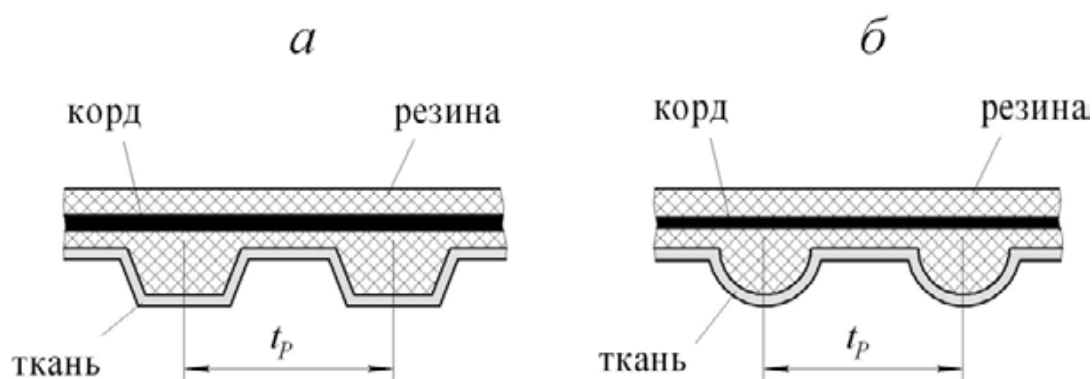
Сборочный зубчатый ремень: *а* – ремень с трапецеидальным зубом; *б* – с полукруглым зубом
